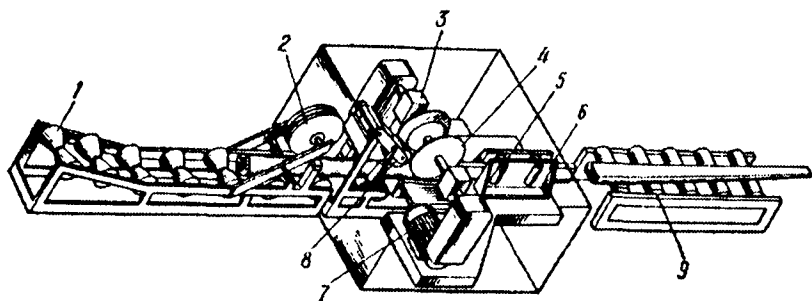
Фрезерно-брусующий станок модели ФБС-750:
